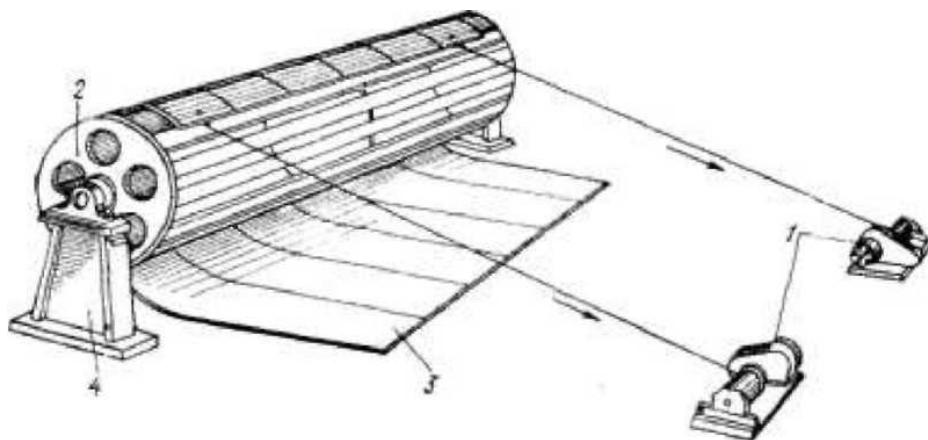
Поворотное приспособление для кантовки полотнищ на 180°
